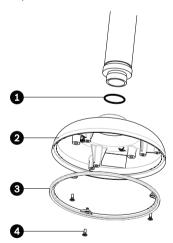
Colocação da junta circular e do anel de retenção para instalação exterior
